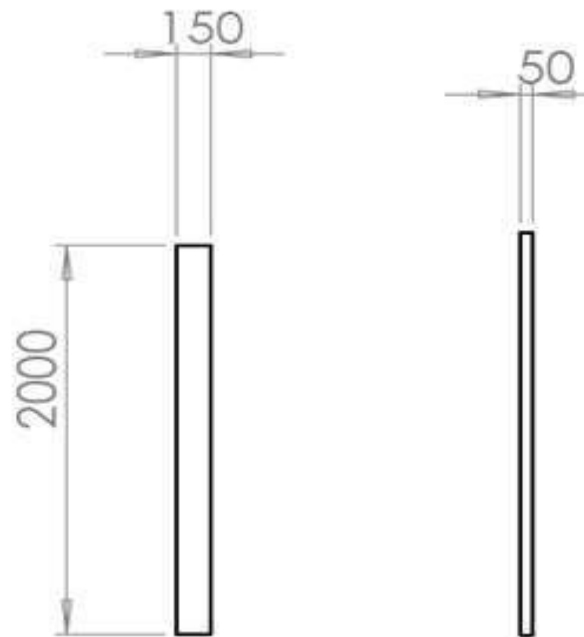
Vista frontal y lateral de la Columna de apoyo tubo rectangular (Omega)
